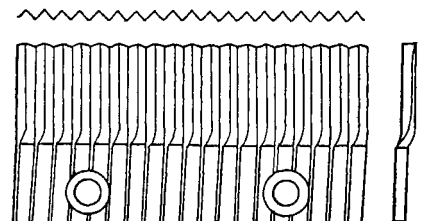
Gefrästes Königsfelder Messer mit Schneide von unten.
